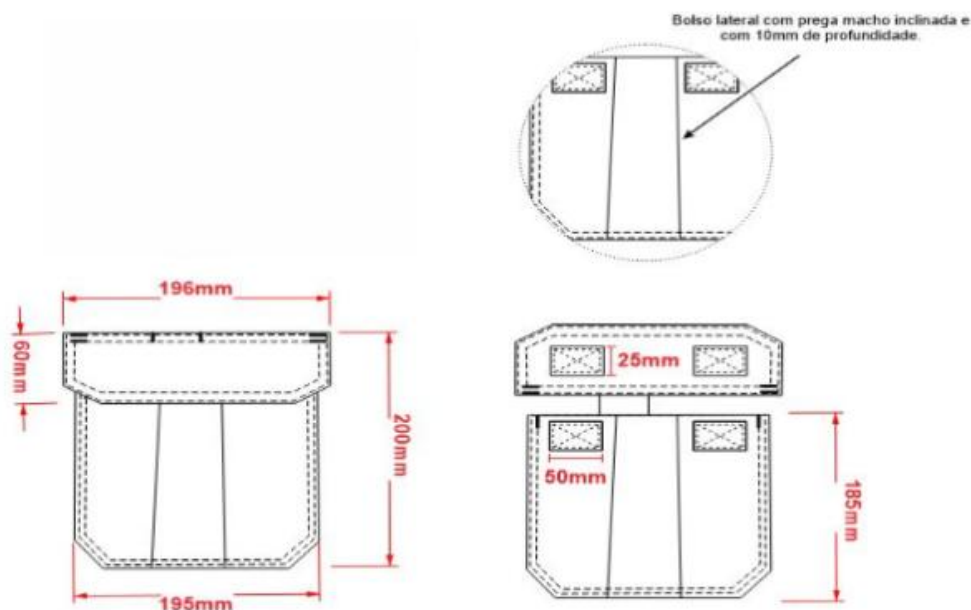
Detalhes do forro dos bolsos dianteiros superiores e laterais, localização da etiqueta de conservação e abotoamento interno (medidas em mm)
